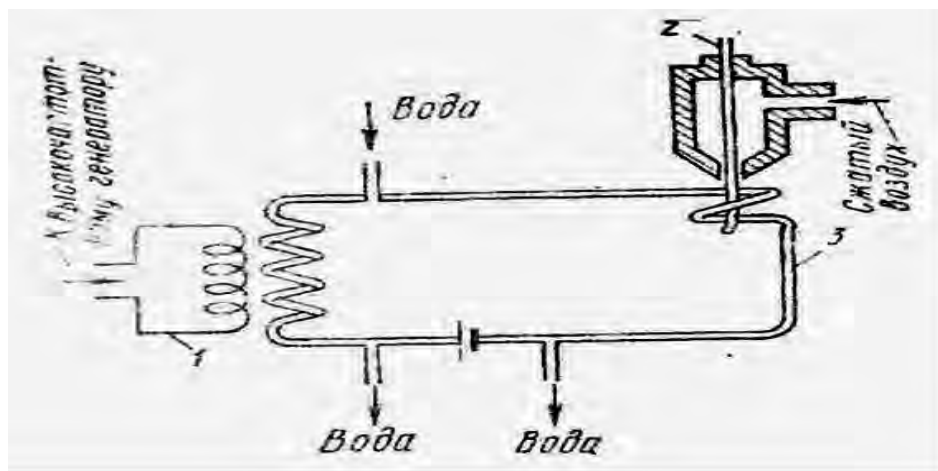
Принципова схема пальника для високочастотного індукційного наплення.
